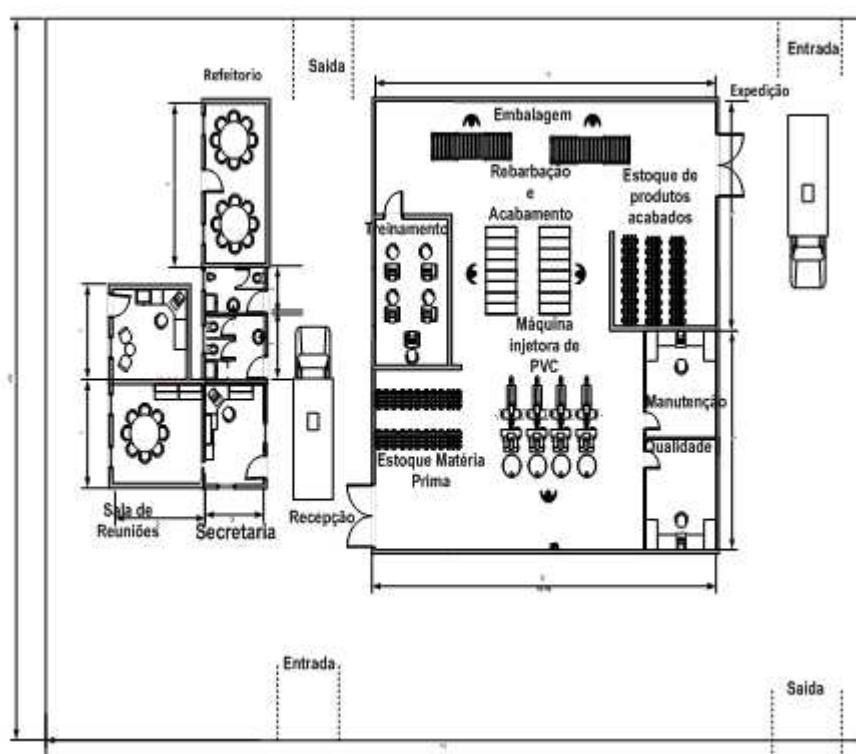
Proposta de Layout para a Mão Mecânica
